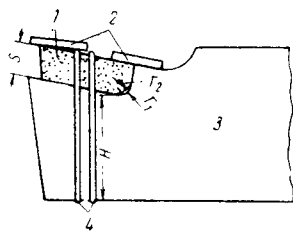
Подготовленные к пайке твердосплавная пластина и державка резца ($H > 3s$); r_1 на державке меньше r_2 на пластинке):
